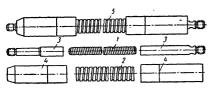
Передача с гибким проволочным валом: 1 — гибкий вал; 2 — броня; 3 — наконечник вала; 4 — арматура брони; 5 — передача в сборе
